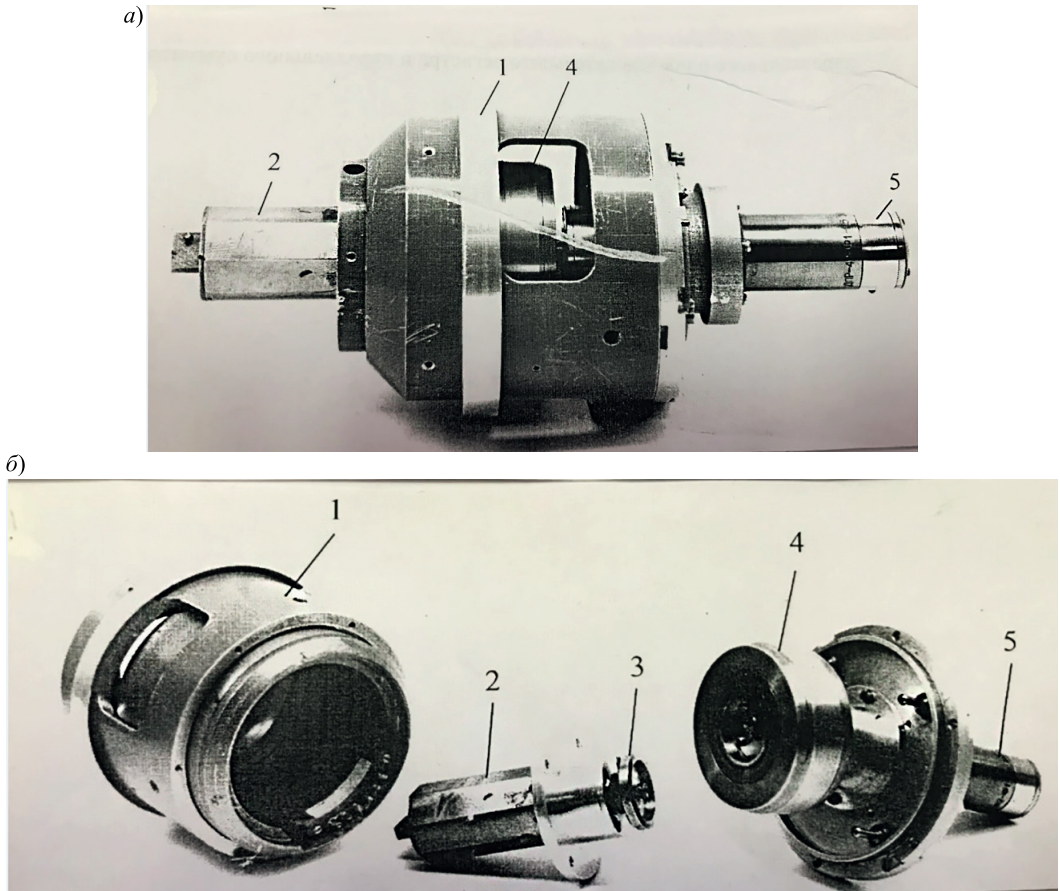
Общий вид и основные сборочные единицы ИУП с шарикоподшипниковым подвесом ротора:
